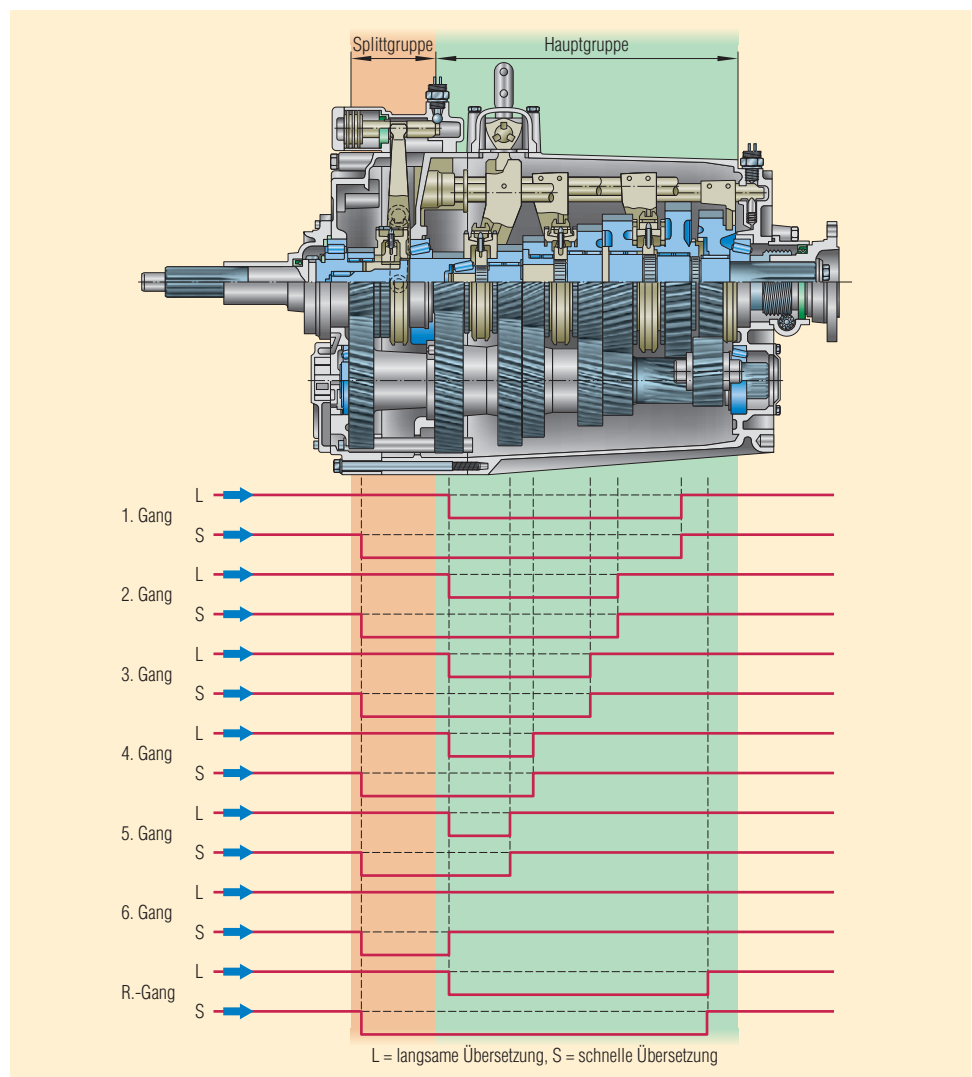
Gruppengetriebe mit Vorschaltgruppe.
